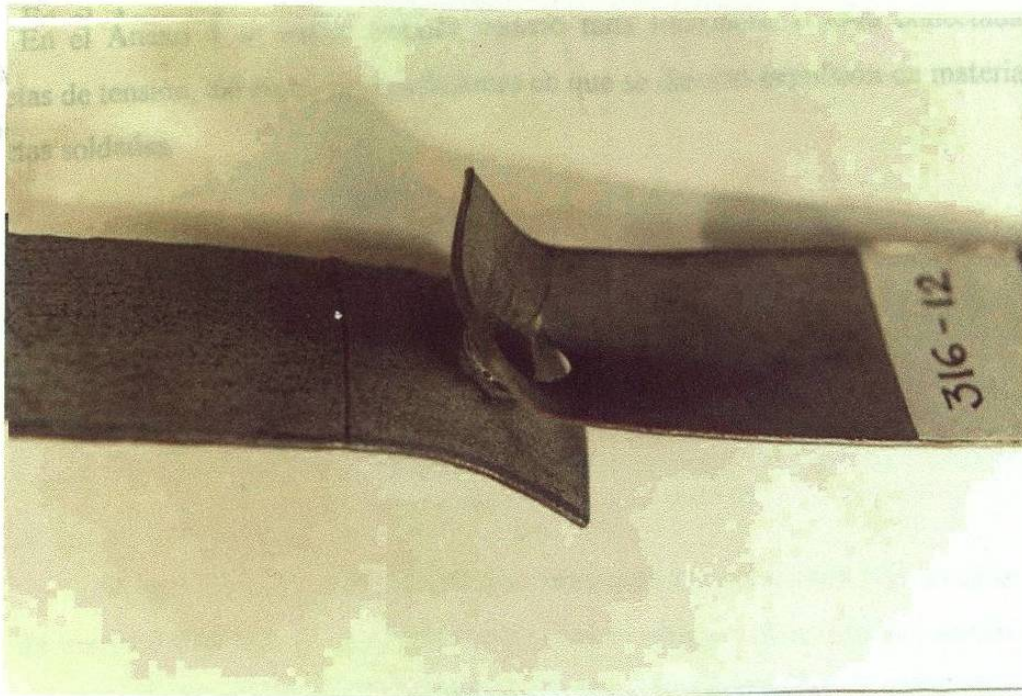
Probeta de tensión de la muestra A soldada con 9.84 kA.
